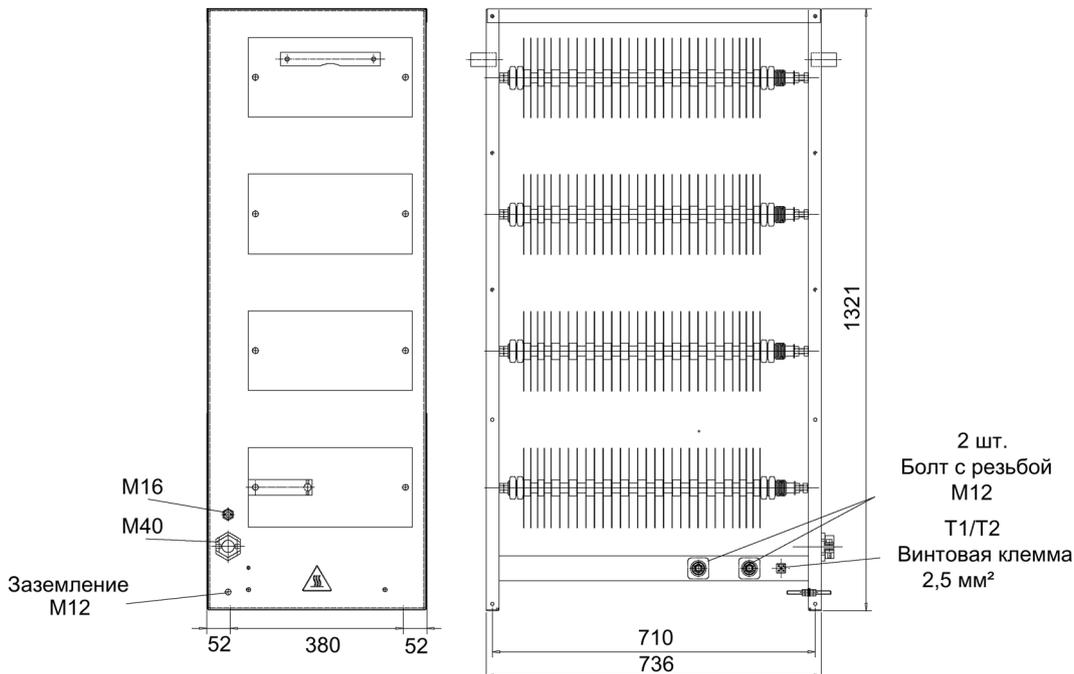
Габаритный чертеж тормозного сопротивления 50 кВт
